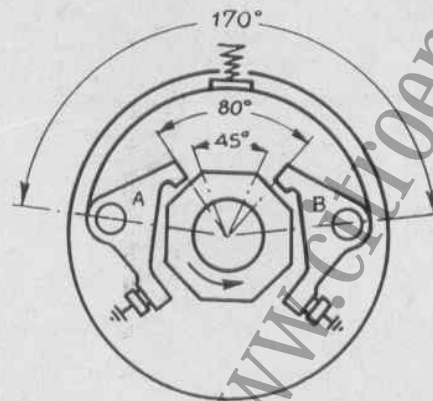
CALAGE DU DISPOSITIF DE RUPTEUR.
